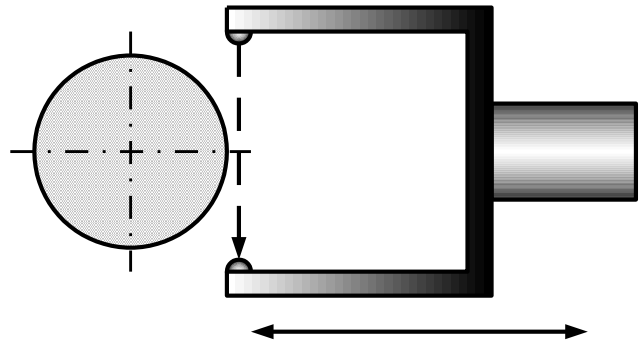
Фотоелектричний однобічний тіньовий вимірювальний пристрій
